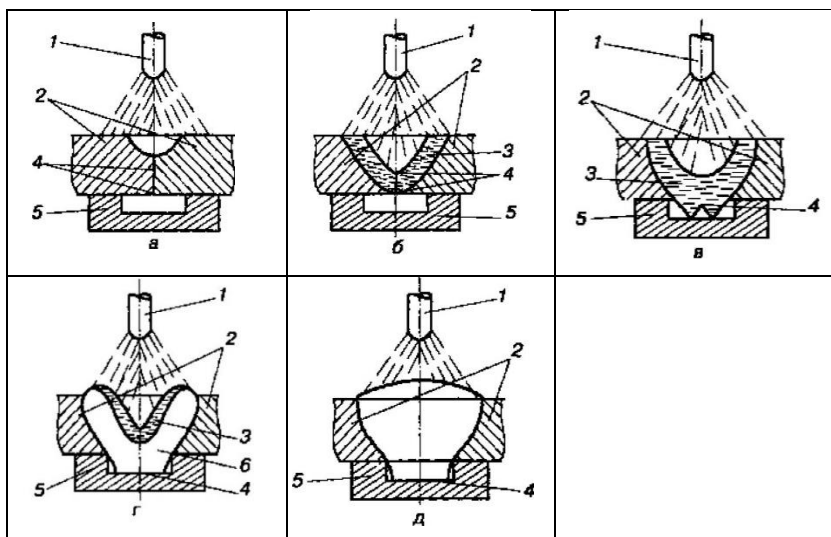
Схема удаления оксидных плен из корня шва при односторонней сварке стыковых соединений на подкладке с канавкой:
